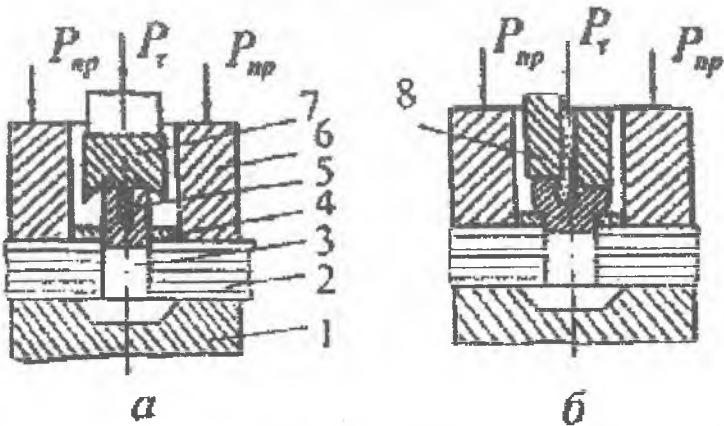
Двухпереходная гидродинамическая клепка из КМ и смешанных пакетов: а – 1-ый переход: 1 – поддержка; 2 – пакет; 3 – стержень полупустотелой заклепки; 4 – кольцо-шайба; 5 – жидкость в полости заклепки; 6 – прижим; 7 – обжимка; б – 2-ой переход: 8 – обжимка второго перехода
